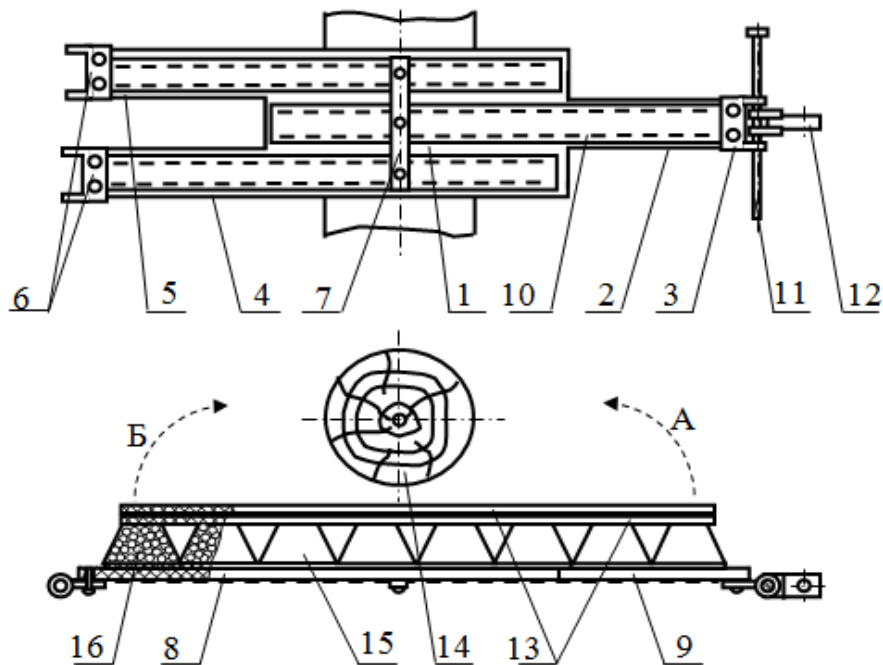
Адаптивна самозатискна петля-захват тросового струшувача: А, Б – напрями охоплення штамба рукавами; 1 – еластична основа; 2 – правобічний рукав; 3 – шарнір правобічного рукава; 4 – нижня гілка лівобічного рукава, 5 – верхня гілка лівобічного рукава; 6 – шарніри лівобічних рукавів; 7 – пластина; 8 – прогумований пас лівобічних рукавів; 9 – прогумований пас правобічного рукава; 10 – скоби; 11 – палець; 12 – кронштейн, 13 – еластичні стрічки; 14 – штамб дерева; 15 – оболонка; 16 – сипкий наповнювач.
